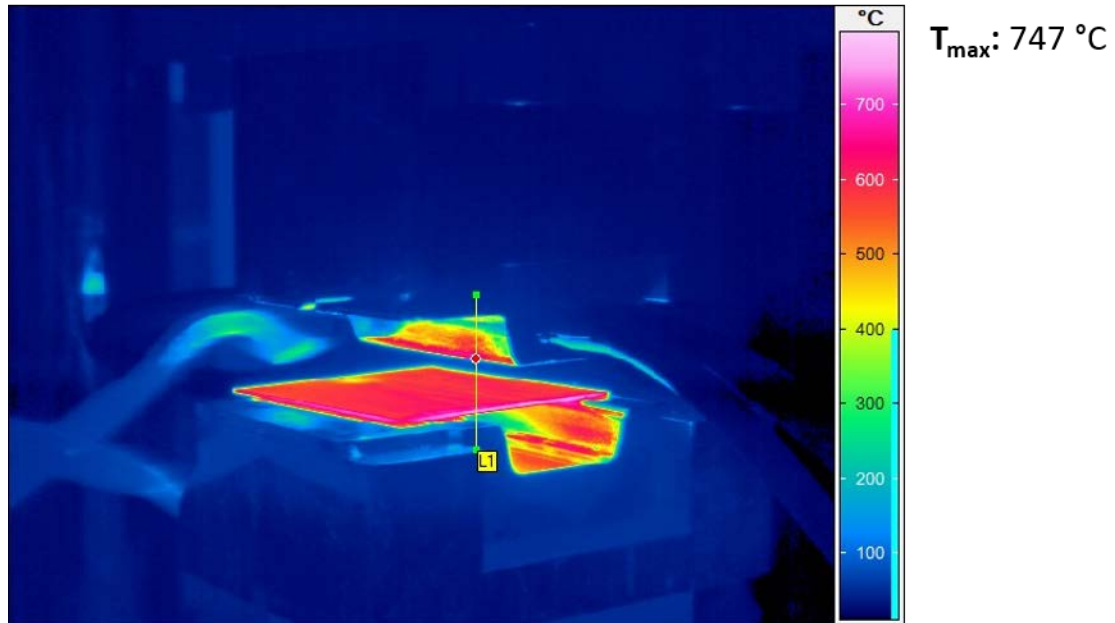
IR-Aufnahme des Bleches im Werkzeug kurz vor der Umformung.
